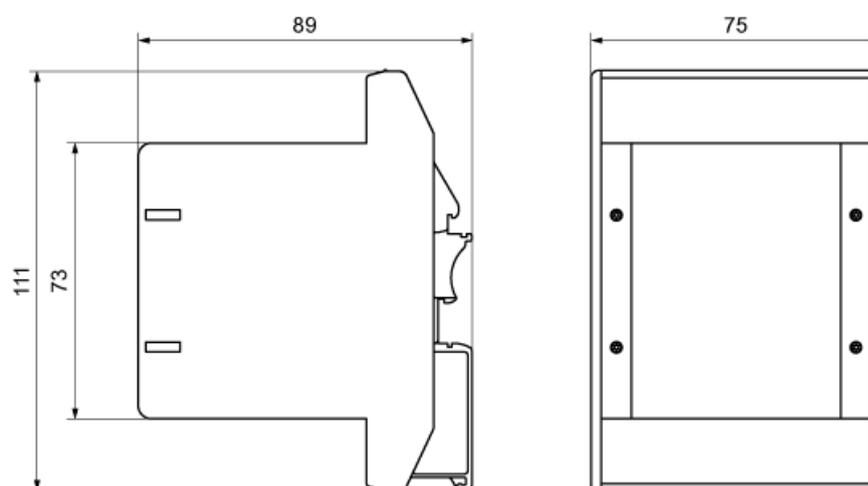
Disegno quotato Safe Brake Adapter (indicazioni in mm)
